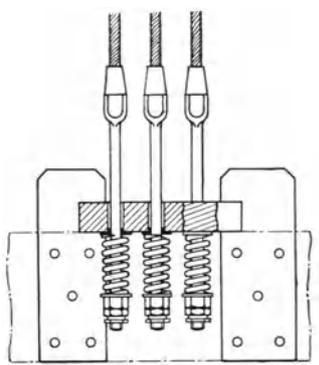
Seilbefestigung am Fahrkorb unter Einschaltung von Federn.
